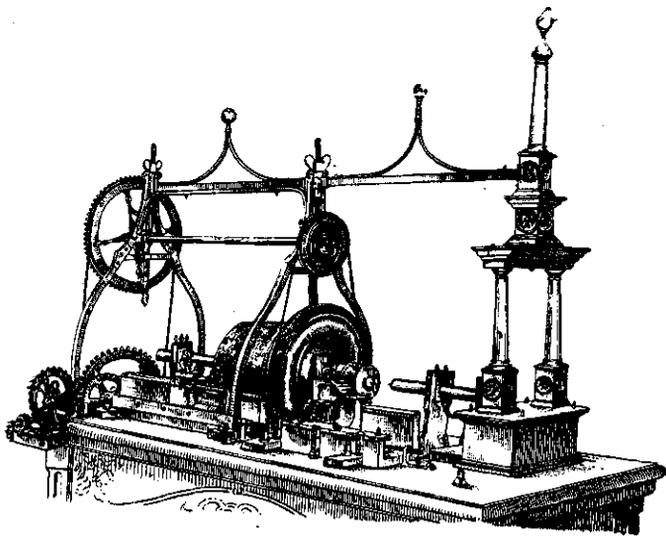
Большой токарно-копировальный станок Нартова 1718—1729 гг. (вид на механизмы привода и супорта).
